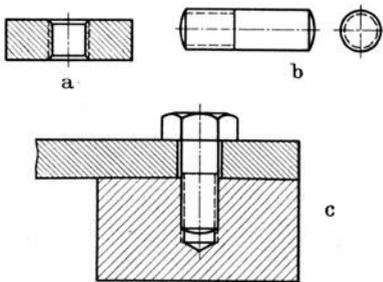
Gewindedarstellung nicht geschnittener Bolzen.
